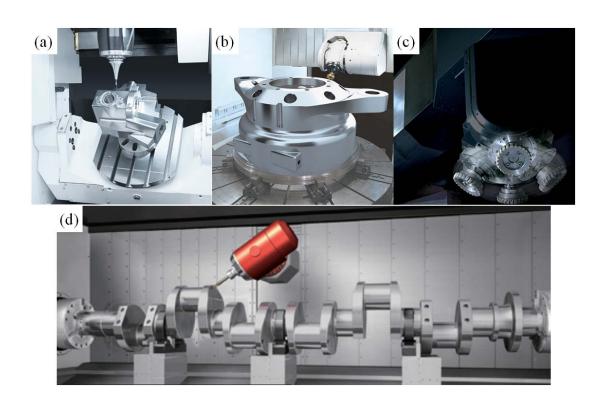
五軸 CNC 之不同軸向配置機型: (a) Table / Table 五軸 CNC 加工機; (b) Head / Table 五軸 CNC 加工機; (c) Head / Head 五軸 CNC 加工機; (d) 車銑複合加工機。[來源: MAZAK、DMG]
